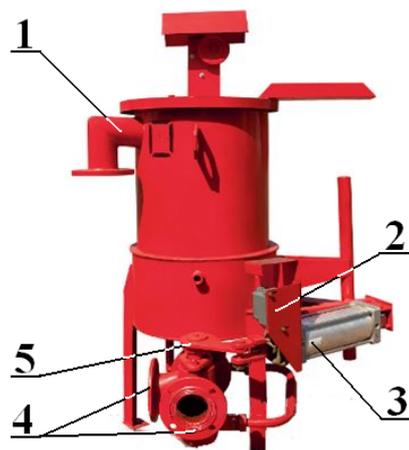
Внешний вид дозатора битума: 1 – заливной патрубок; 2 – блок управления дозированием; 3 – механизм закрывания сливного крана; 4 – фланцы сливного патрубка; 5 – сливной кран
